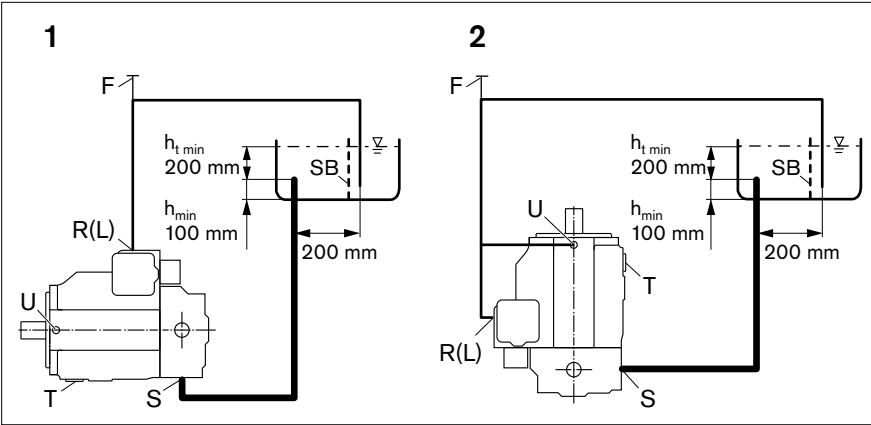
Untertankeinbau mit waagrechter Einbaulage 1 und senkrechter Einbaulage 2
